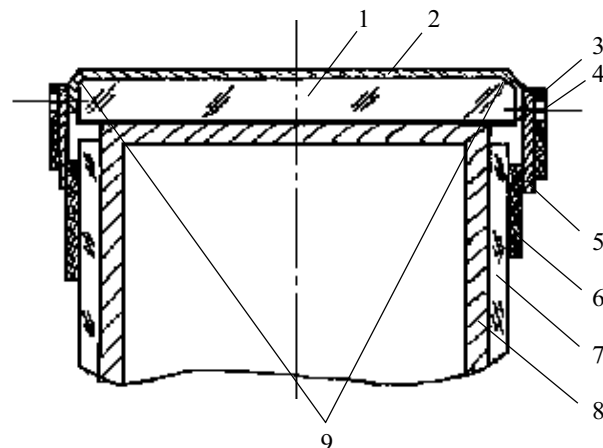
Конструкция фотоприемного модуля для МФР: 1 — ТТЭП; 2 — координатная шина; 3 — полиимидная пленка; 4 — окно в пленке для микросварки; 5 — алюминиевая полоска; 6 — БИС; 7 — печатная плата; 8 — корпус фотоприемного модуля; 9 — фаски (5 мкм)
